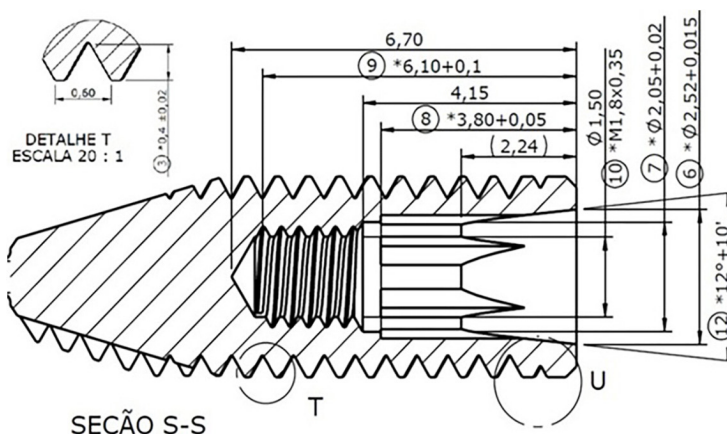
Projeto do Implante CM Cilíndrico 3,75 × 11 mm (ref. 100.117) SINGULAR Implants®.
